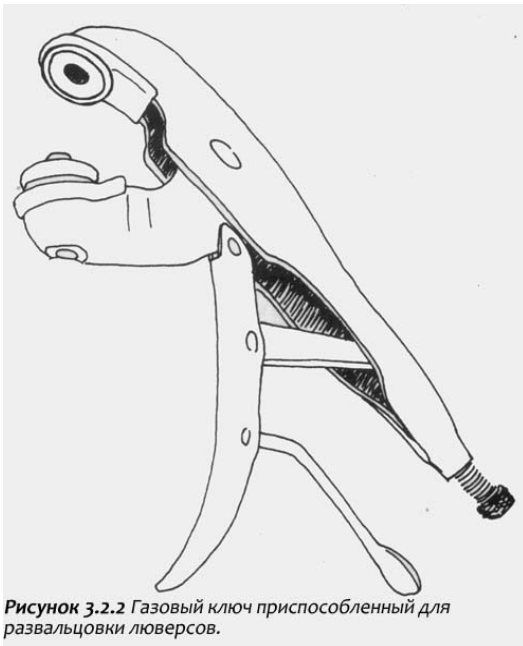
Газовый ключ приспособленный для развальцовки люверсов.
